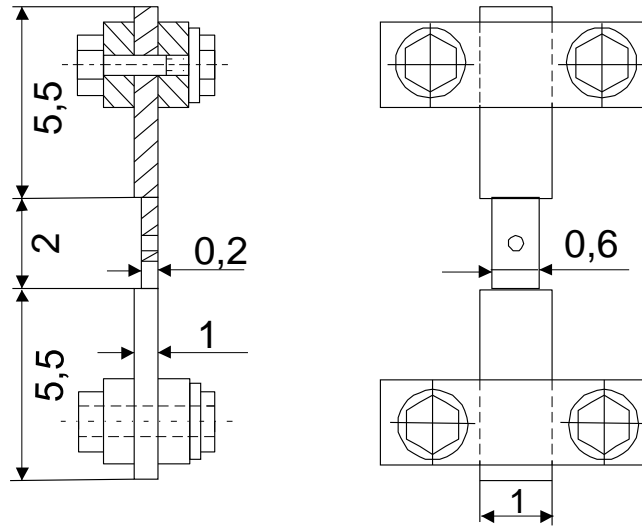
Схема устройства пластинчатого силитового нагревателя (Михайлов, Шацкий, 1974). Размеры деталей нагревателя в см.
